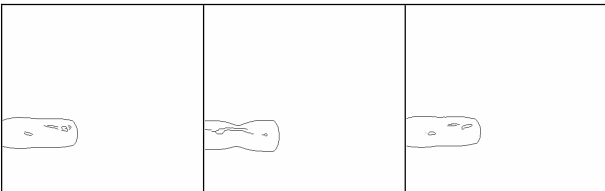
'de sağlam bir kesici takım, Şekil-2 ve Şekil-3'de ise aşınmış iki kesici takım için elde ardışıl imge çerçeveleri verilmektedir. Bu üç şekilde görüldüğü gibi aşınmış kesici takımların en büyük özelliği kesici yüzeylerindeki bozulmalardır. Bu bozulmaların tespiti için öncelikle Canny [4] kenar bulma yöntemi ile kenar tespiti yapılmaktadır. Bu yöntem ile elde edilen kesici takım kenar imgeleri Şekil 4-5 ve 6'da verilmektedir. Uygun seçilen Canny eşik parametresi ile arka plandaki bulanık nesnelere, kenarlar imgesinde görülmesi engellenmektedir. Kameranın odak noktası, yakın mesafeleri net alacak şekilde ayarlandığından arka plandaki herhangi bir nesne kenar imgesinde görülmemektedir.
